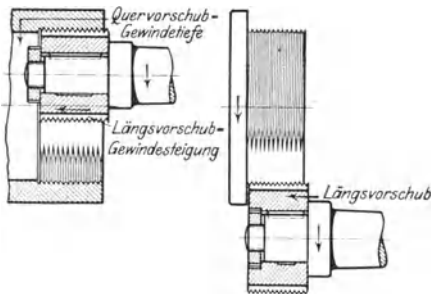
Fräsen von Innen- und Außen-gewinde.
